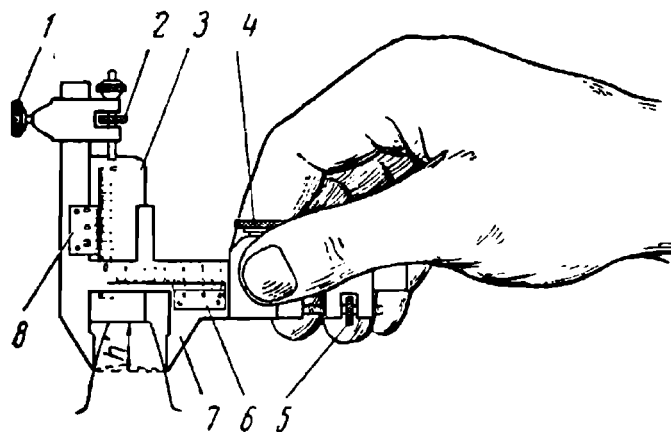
Специальный штангензубомер для измерения толщины зуба
